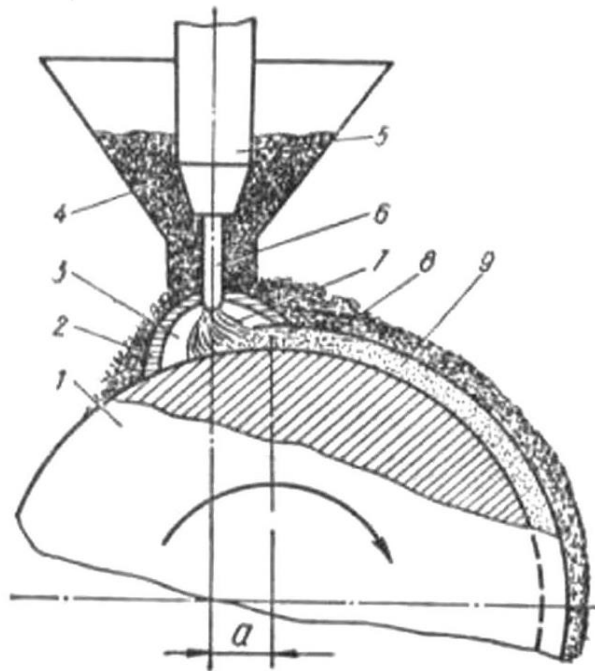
Схема відновлення деталей типу вал наплавленням під шаром флюсу:
